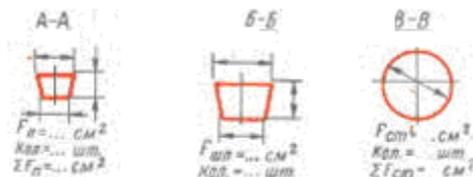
Порядок обозначения размеров элементов литниковой системы
